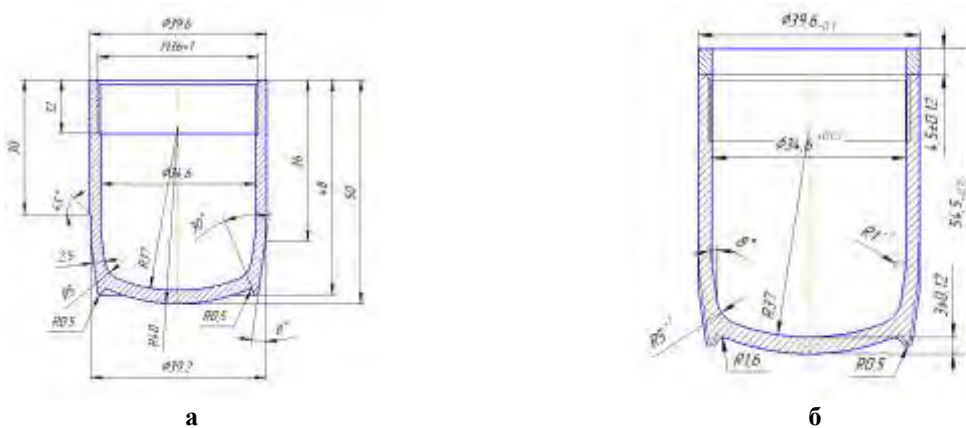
а - креслення деталі; б – креслення деталі з припуском на обрізування
